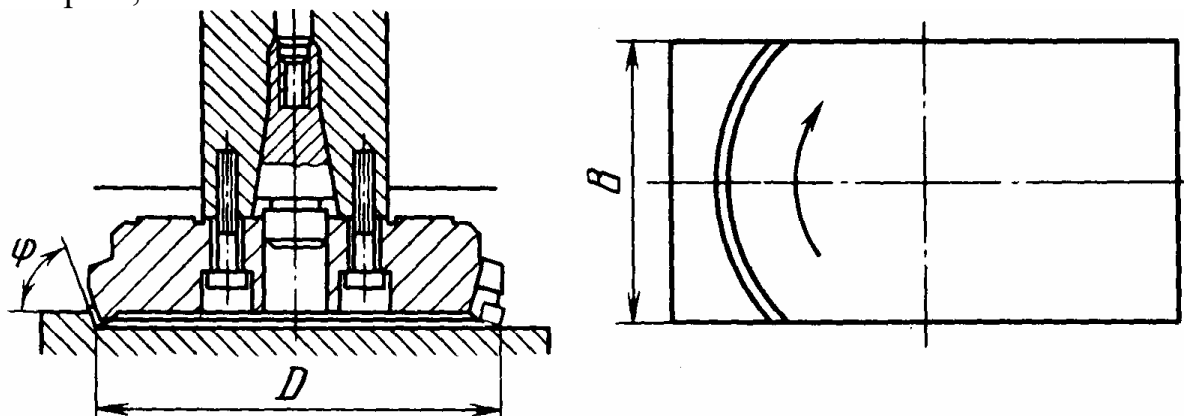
Схема фрезерування відкритих плоских поверхонь за допомогою торцевої фрези
